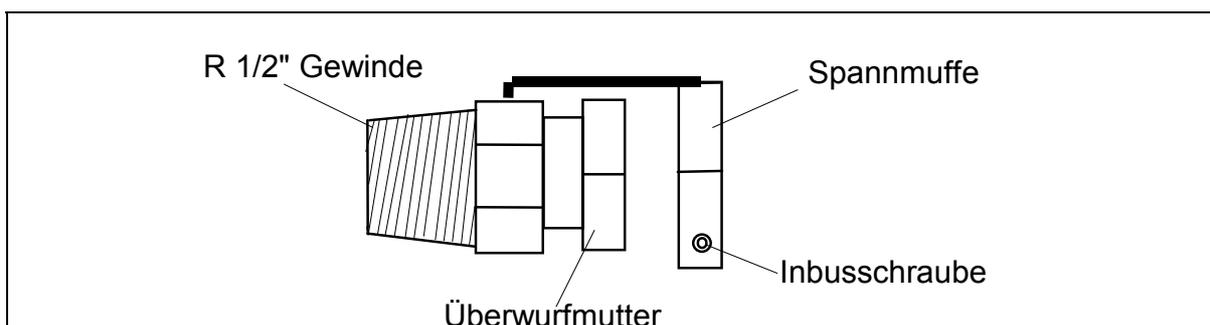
Klemmringverschraubung mit angeschweißter Spannmuffe
